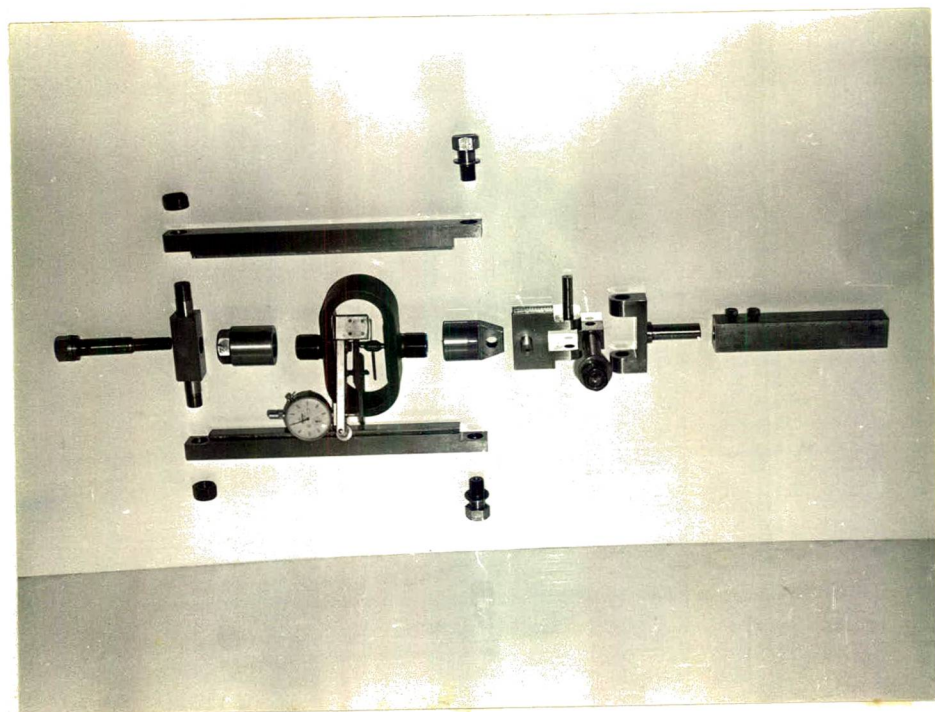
Vista explodida do dispositivo de carregamento do método 2.
